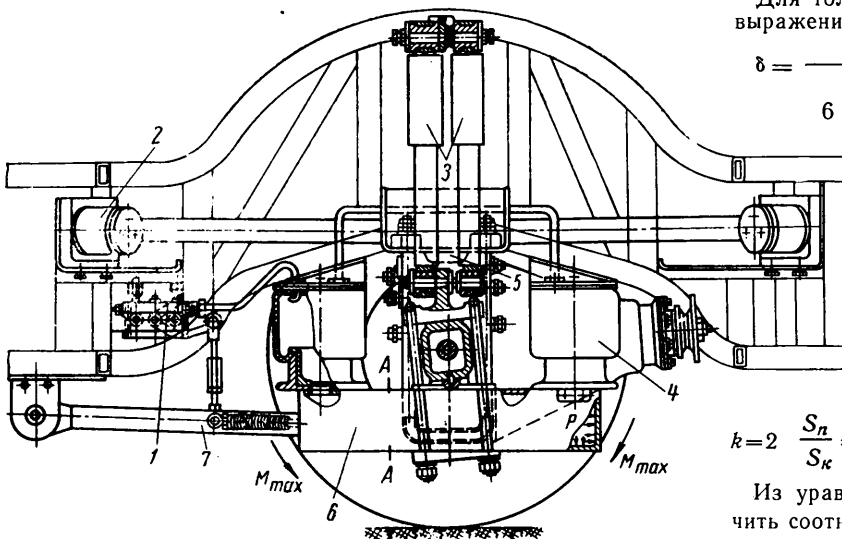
Пневматическая подвеска с балкой-резервуаром:
